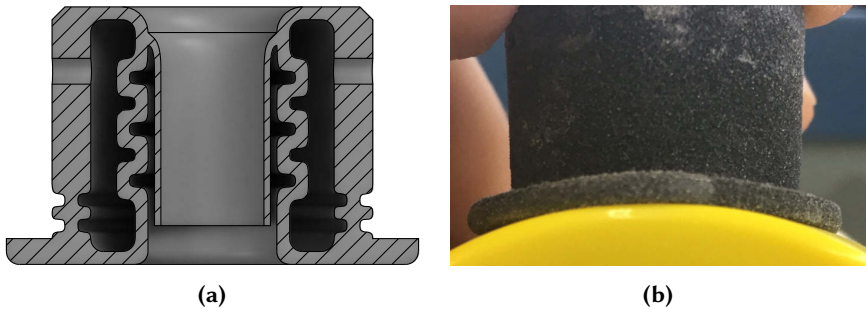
Prototyp einer formflexiblen Düse zur Anpassung an gekrümmte Strukturen; (a) CAD, (b) gedrucktes Bauteil
